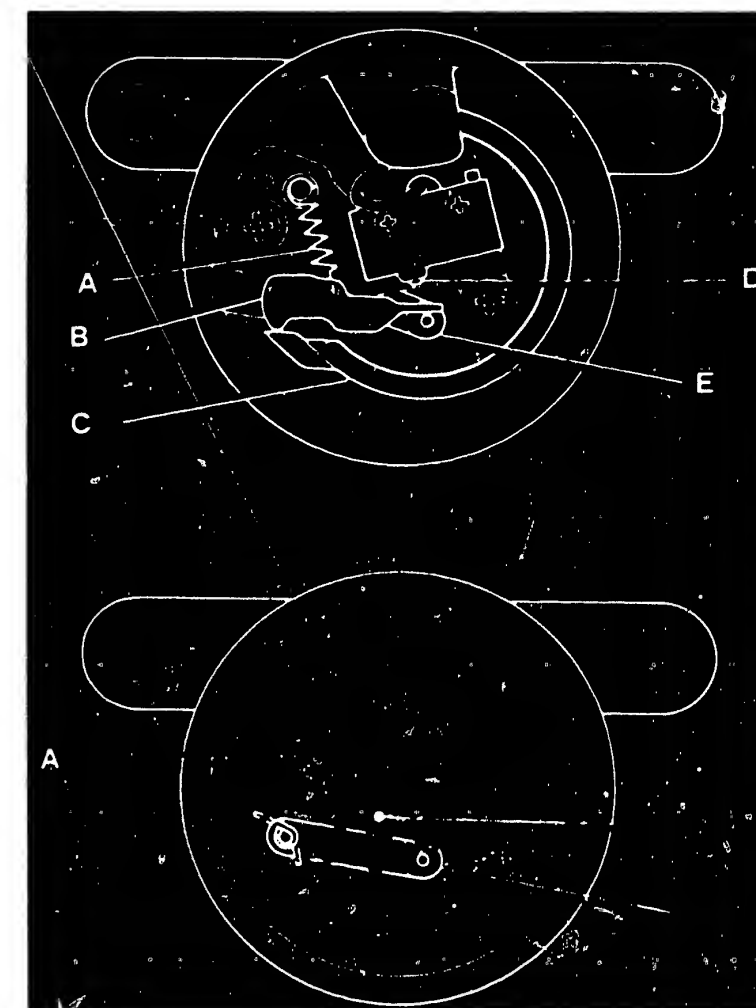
Der Druckschalter in seinen Schaltpositionen. A Feder – B Hebel – C Bourdonische-Röhre – D Mikroschalter – E Hebelarm – G Kontaktschalter
